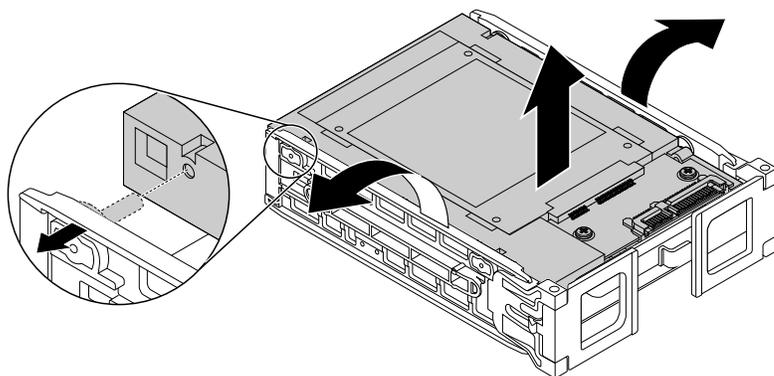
Извлечение конвертера из крепежной скобы типа 1
